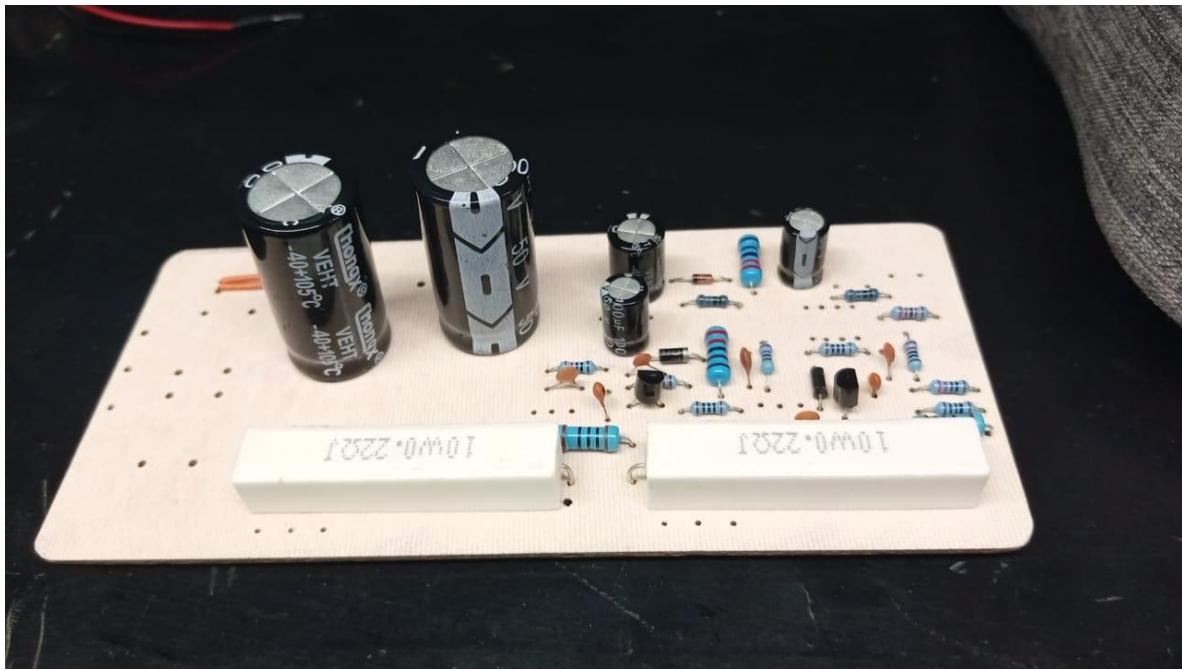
Tercer grupo de componentes soldados a la PCB.
